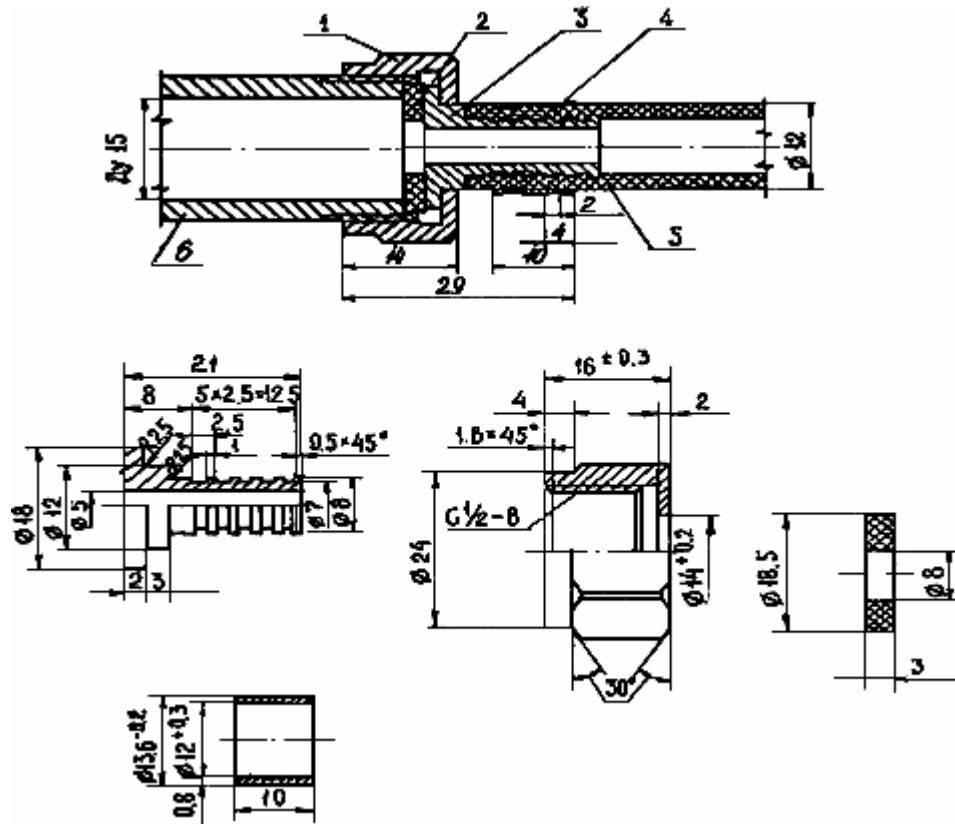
Конструкция полиэтиленовой подводки с ниппельными соединительными узлами:
